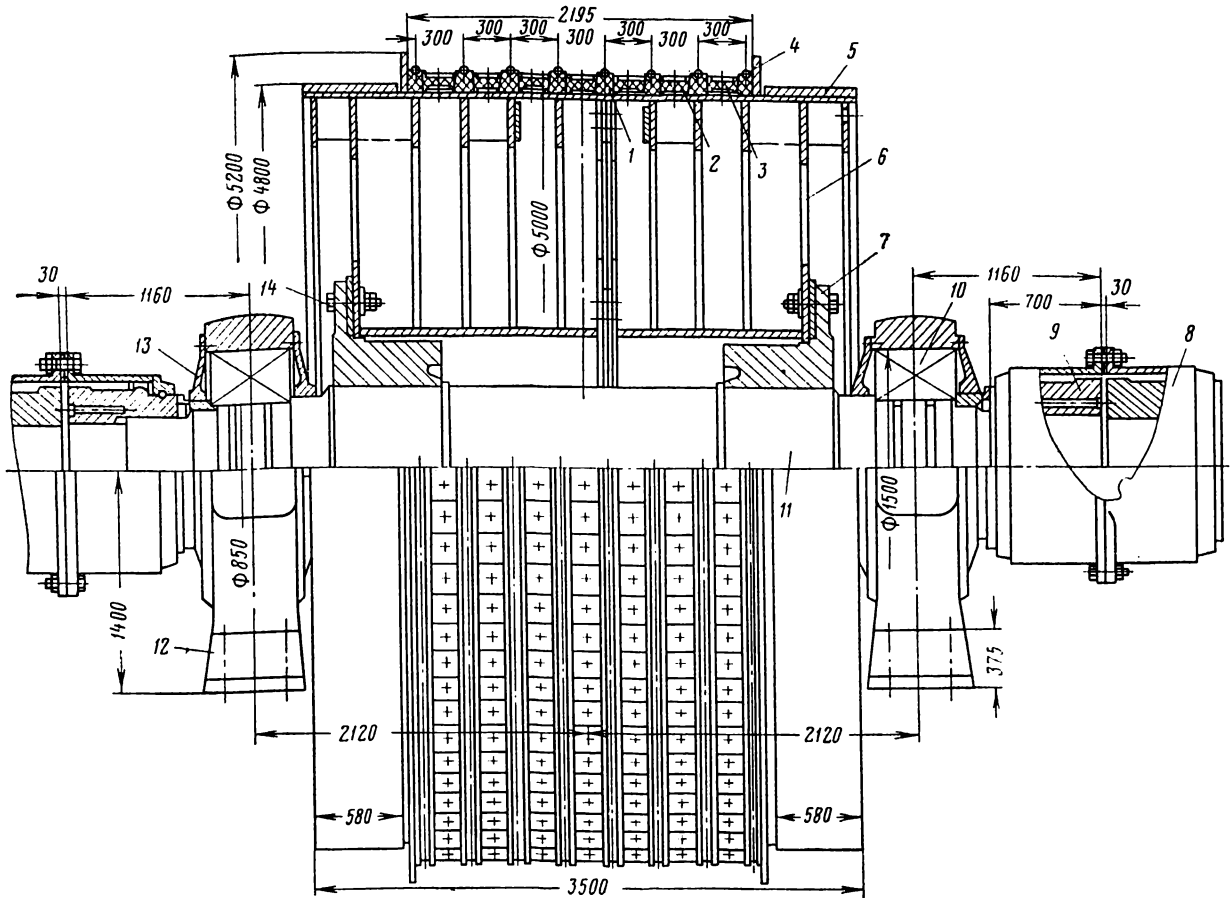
Сборка главного вала машины ЦШ5×8
